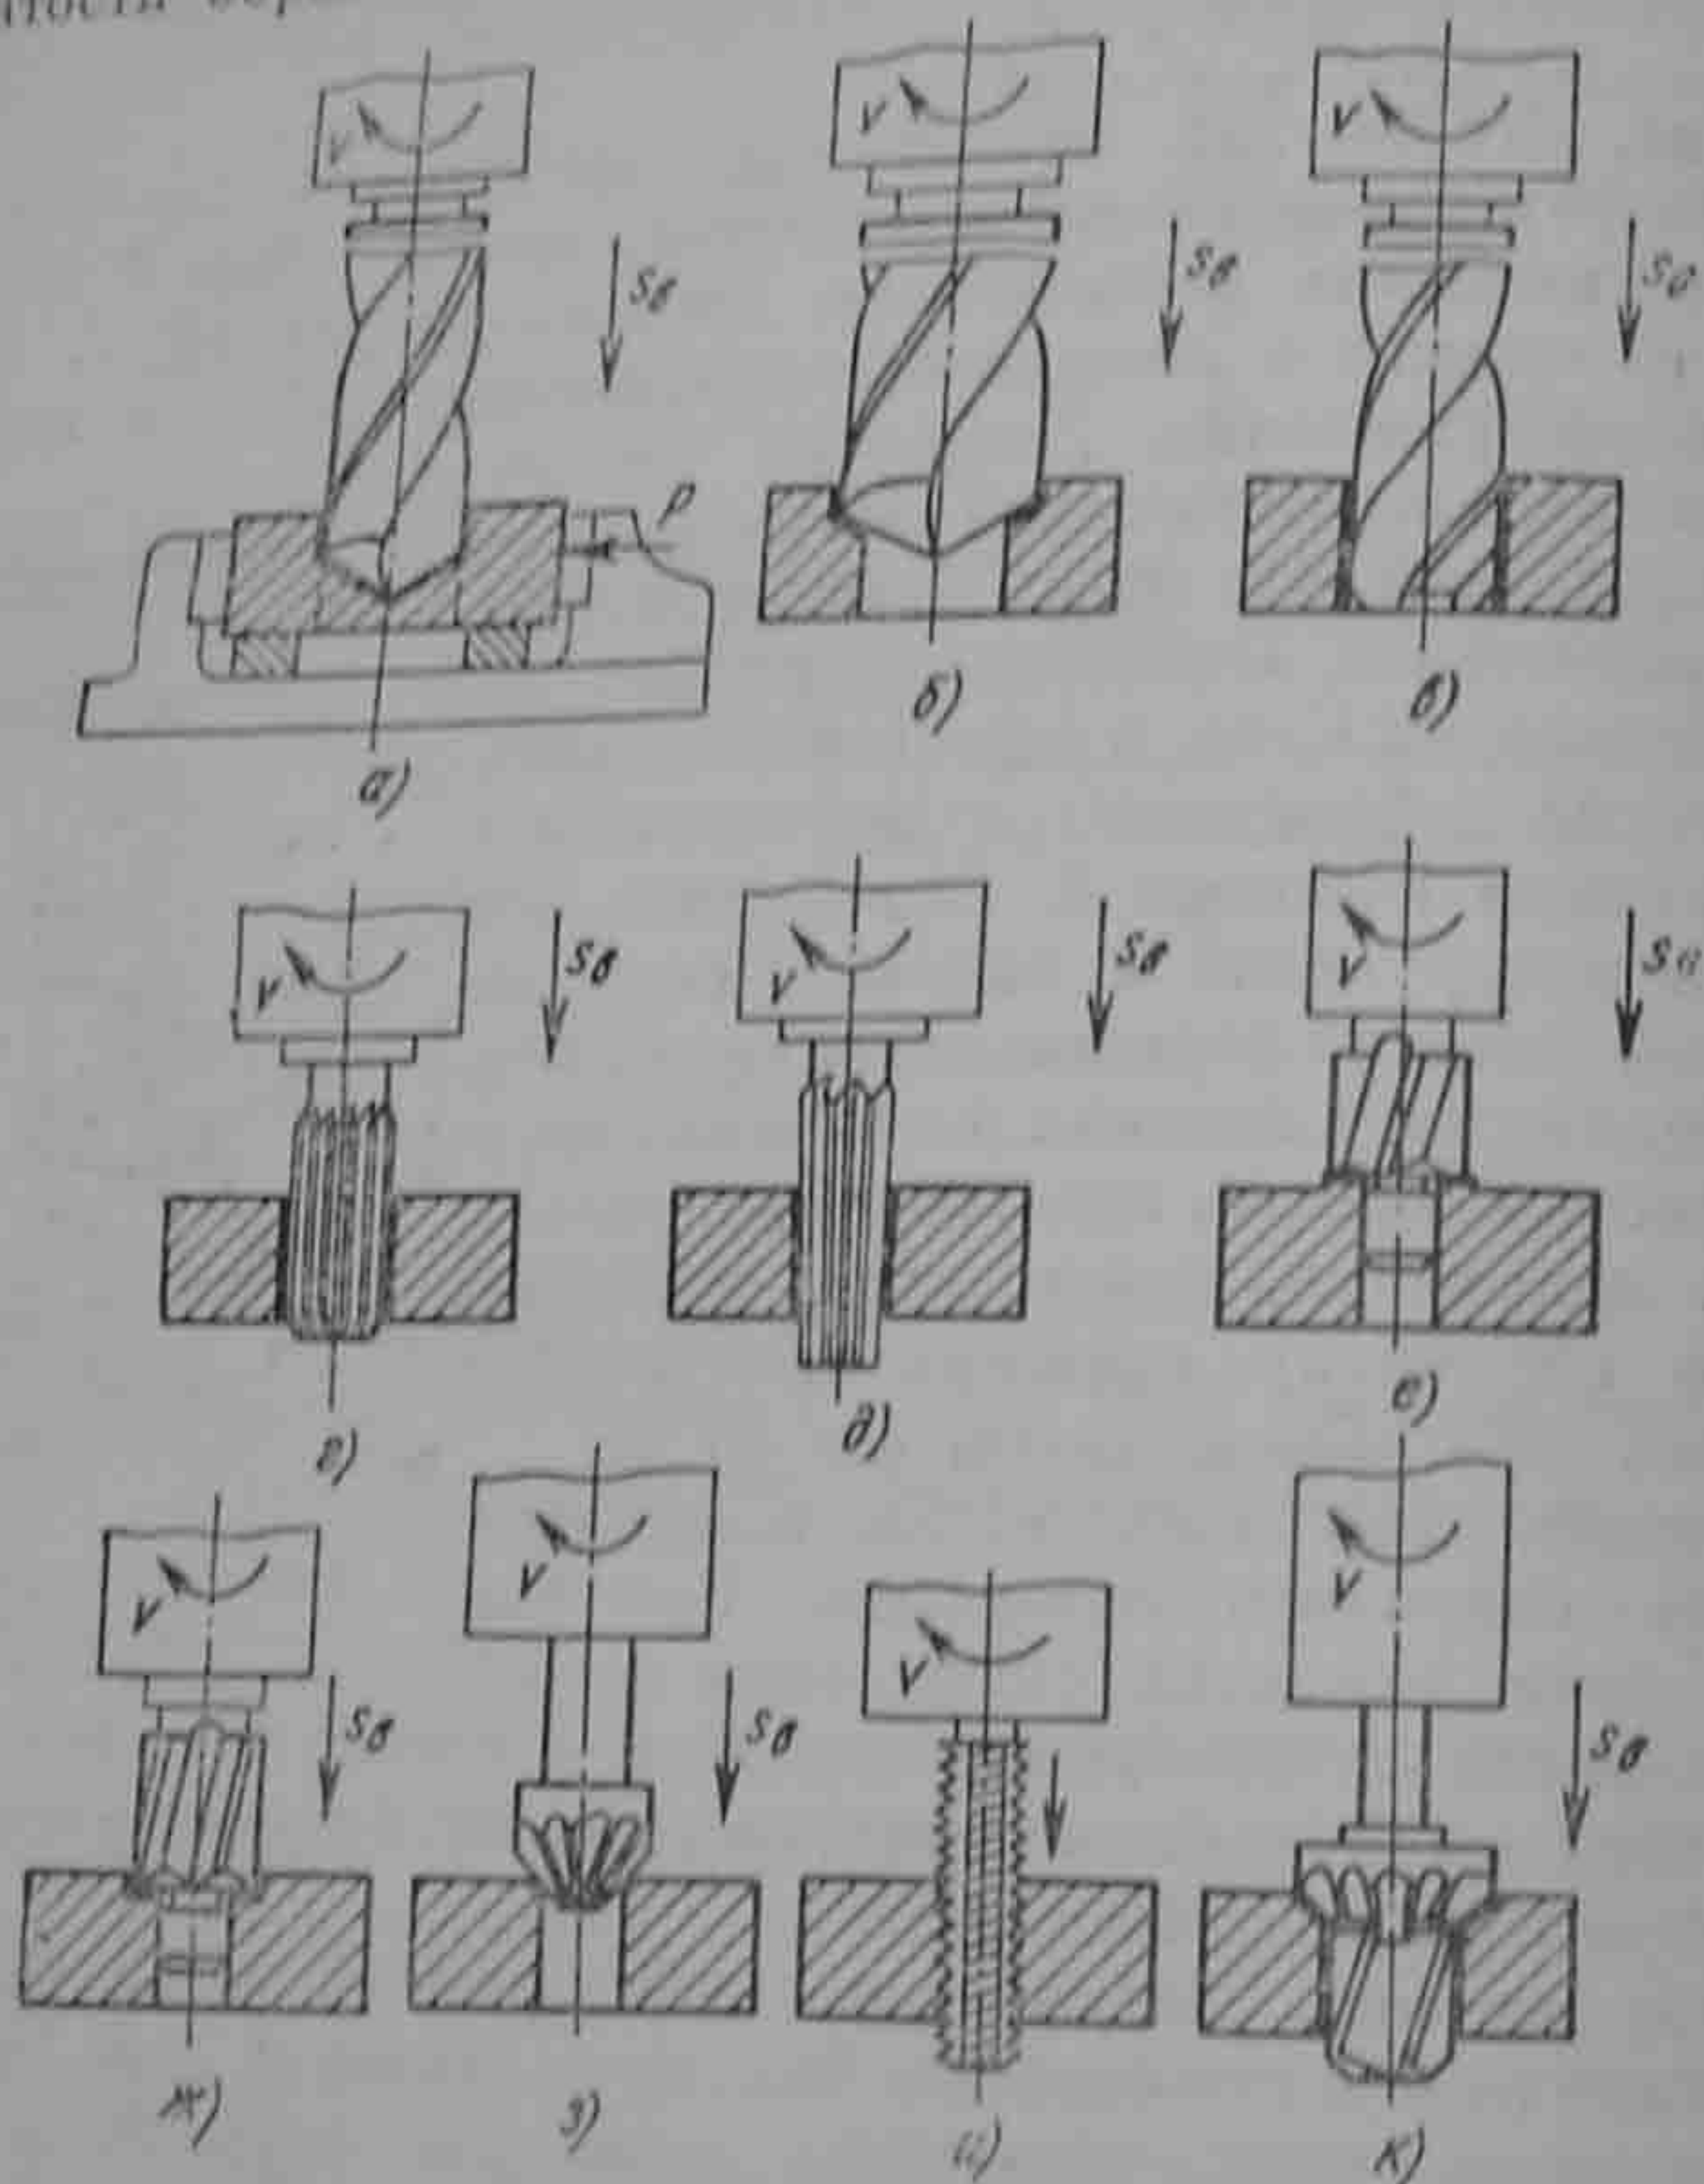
Схемы обработки заготовки на вертикально-сверлильных станках
